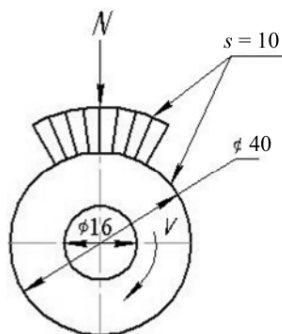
Схема испытаний «вал – частичный вкладыш»
